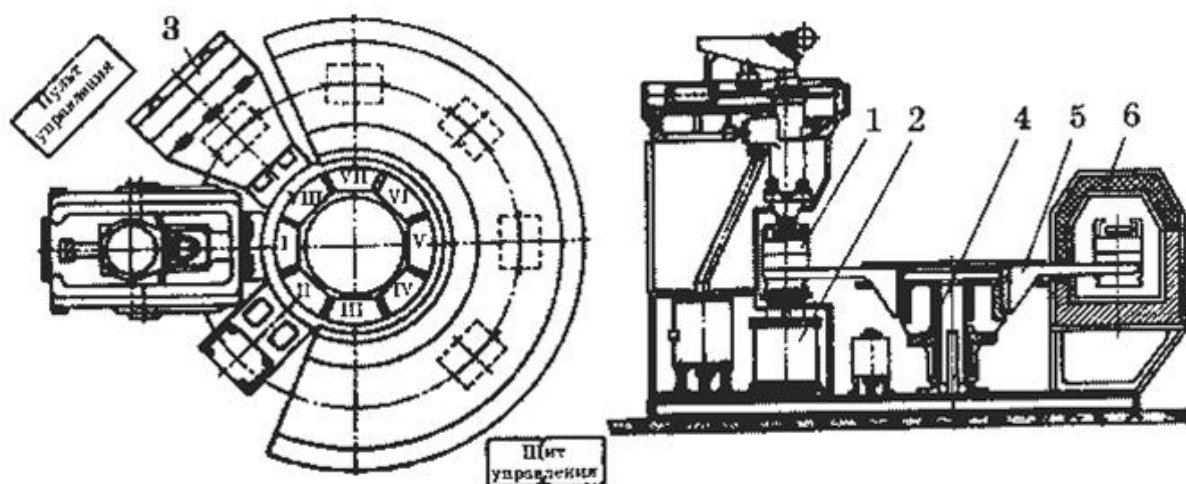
Схема автоматической карусельной пескострельной машины для изготовления стержней в нагреваемой оснастке
